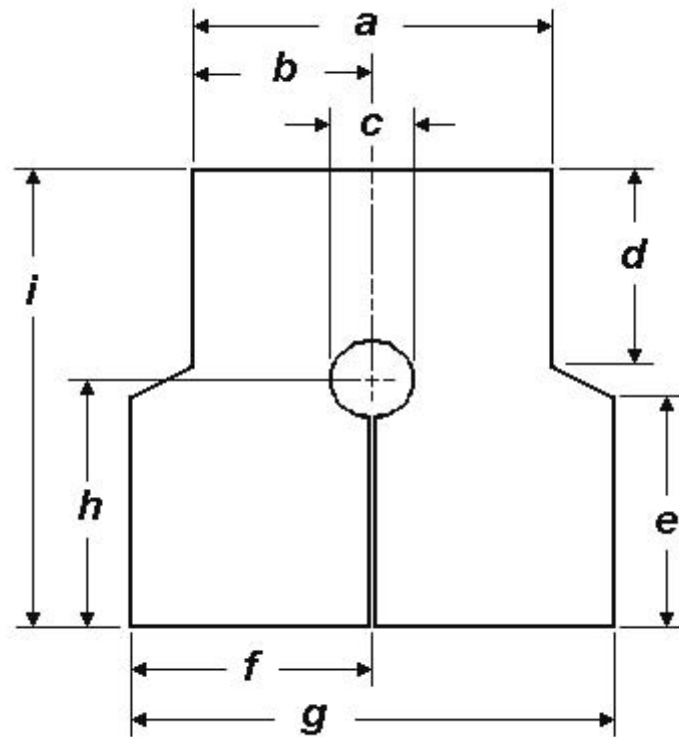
Patrón de corte de la funda (fundas exterior e interior)
